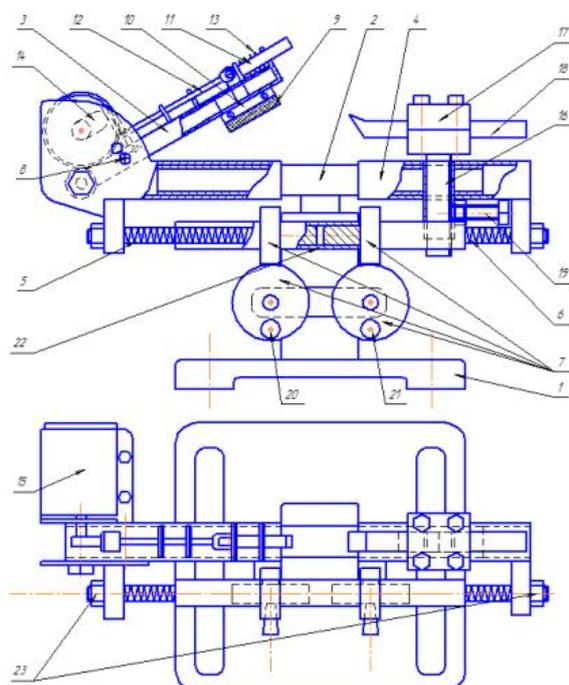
Схема приспособления для шлифования фасок и тарелок клапанов двигателей
